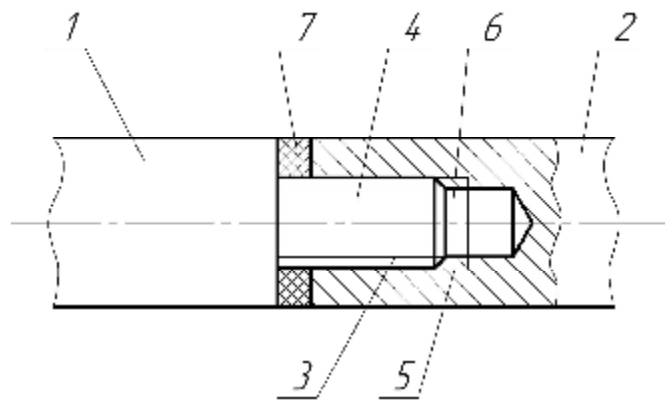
Схема різьбового з'єднання валів з фрикційною шайбою
